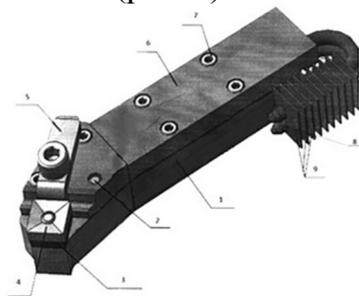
Резец для сухого резания (1-державка;2- палец направляющий; 3-опорная пластина;4-режущая пластина;5-прижим;6-крышка;7-винт; 8-тепловая труба;9-радиатор)
